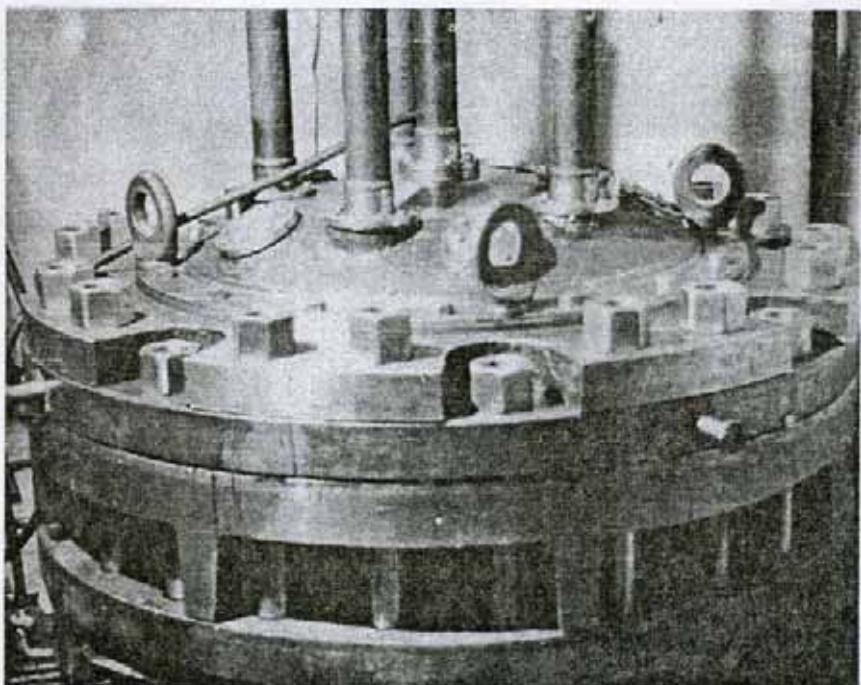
Общий вид технологического блока установки для изготовления крупногабаритных тонколистовых деталей
